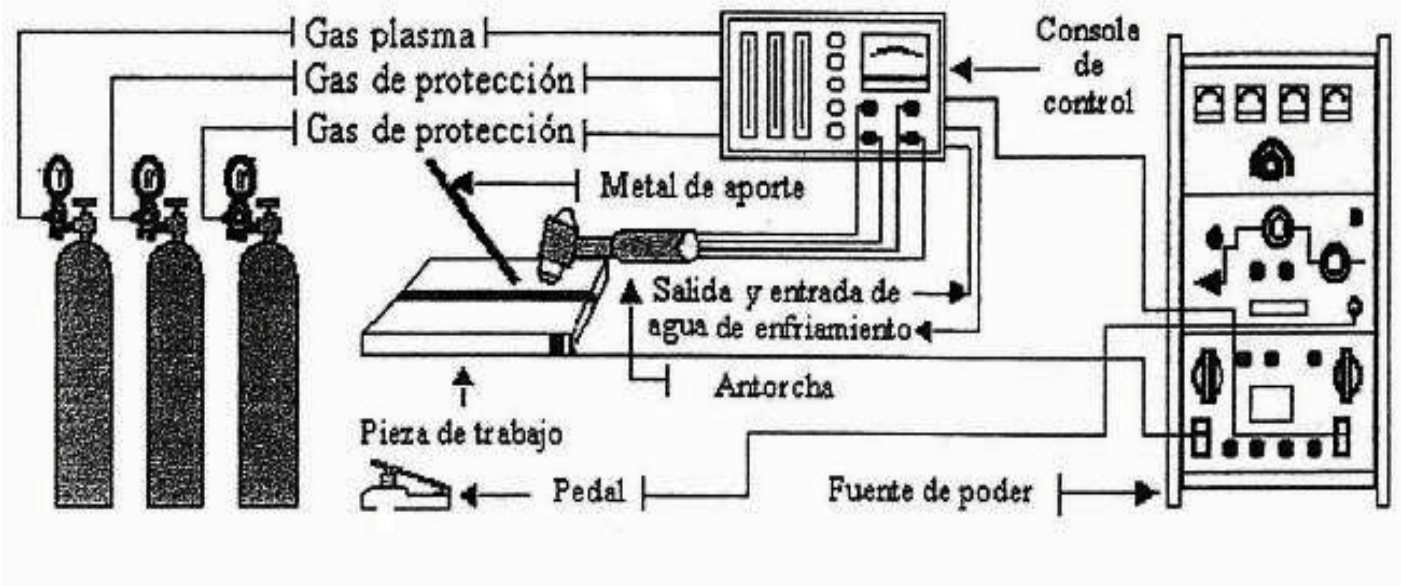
EQUIPO PARA SOLDADURA POR ARCO PLASMA
